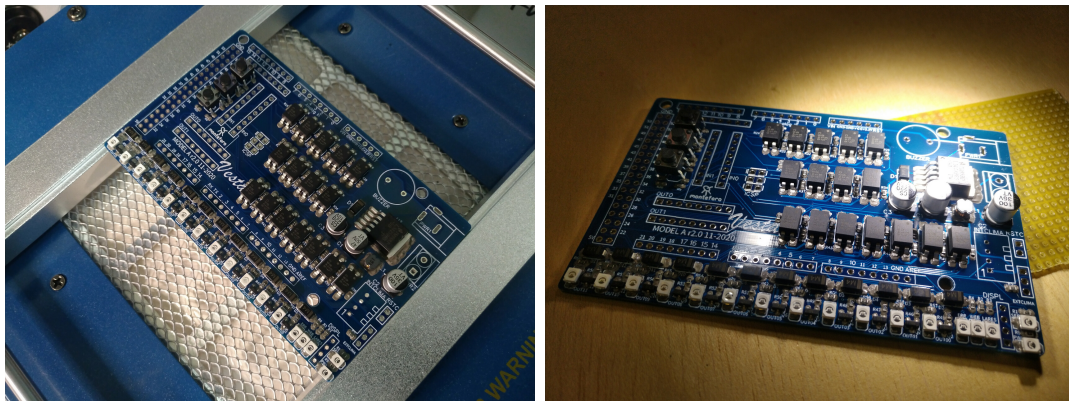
Proceso de soldadura SMD de componentes
